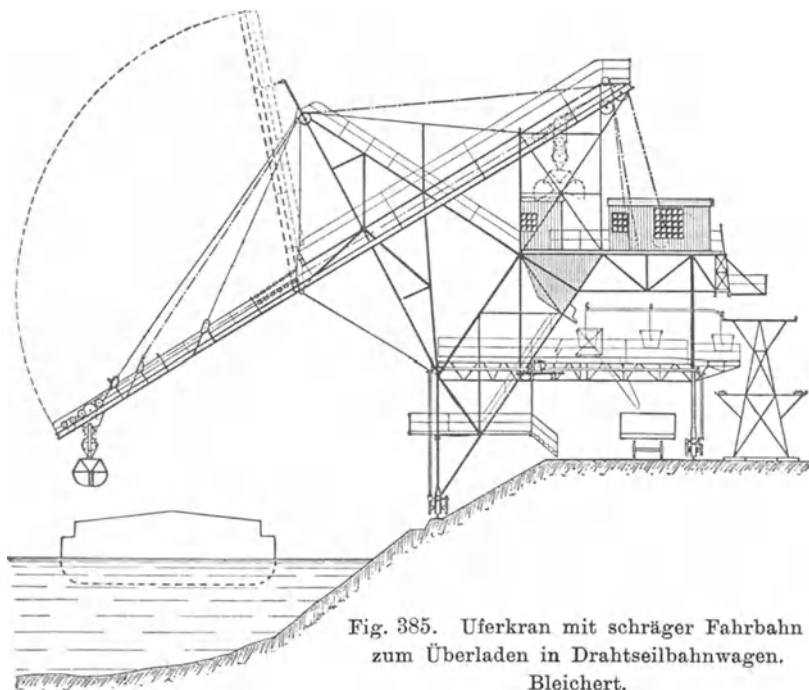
Uferkran mit schräger Fahrbahn zum Überladen in Drahtseilbahnwagen.
